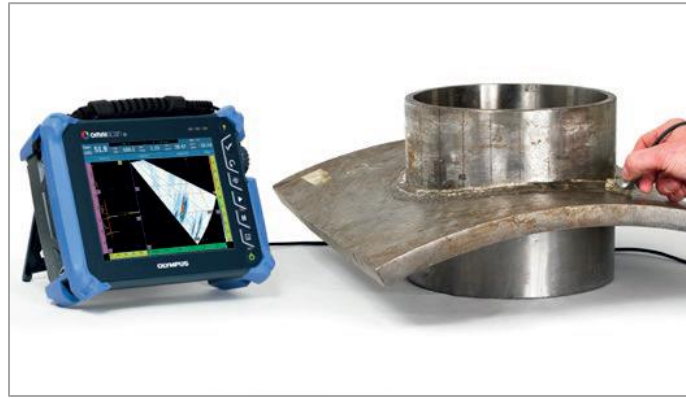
OmniScan SX en inspección de soldadura por arreglo de fases.
